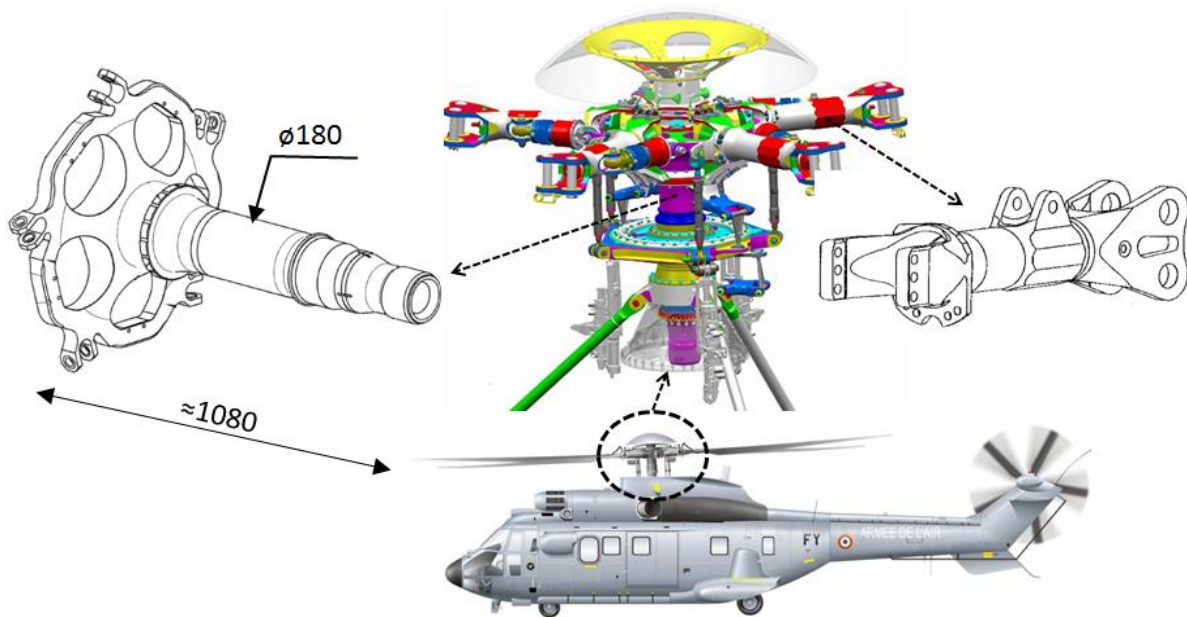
Positionnement du mât rotor et du manchon de fixation de pôle : pièces critiques en 15-5PH usinées en tournage finition.
